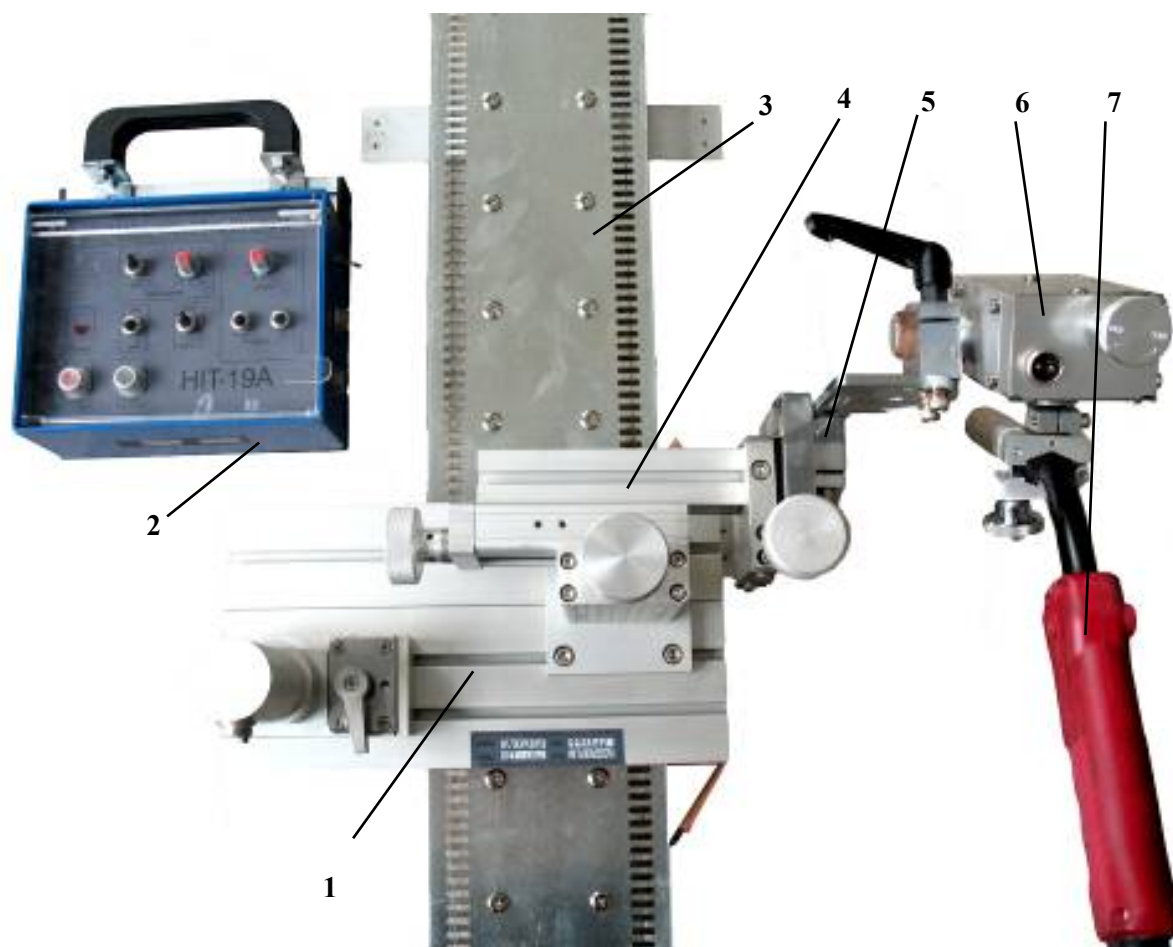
Сварочная каретка HIT-1CW – внешний вид
